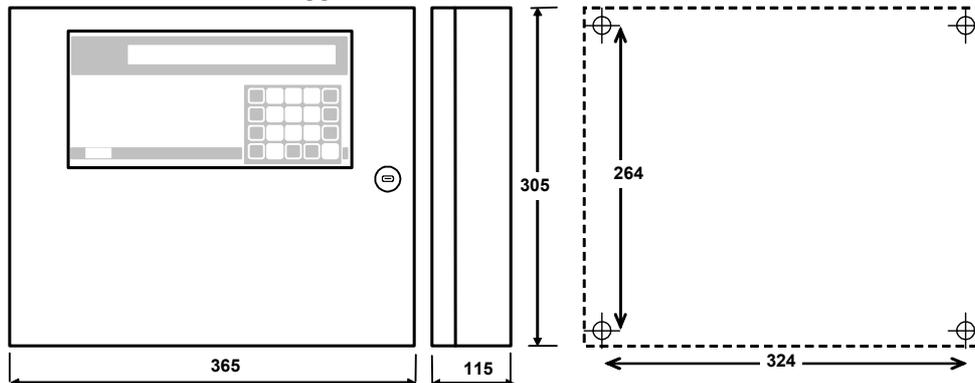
CE608P e CE616 Dimensioni e Dima di fissaggio a parete
